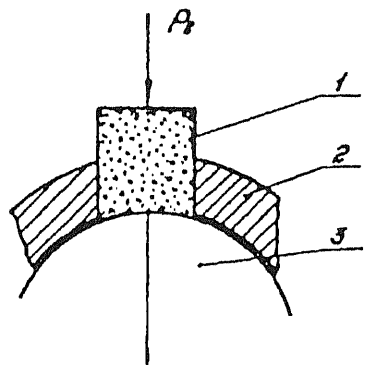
Подшипник, смазываемый по методу ротапринта:
